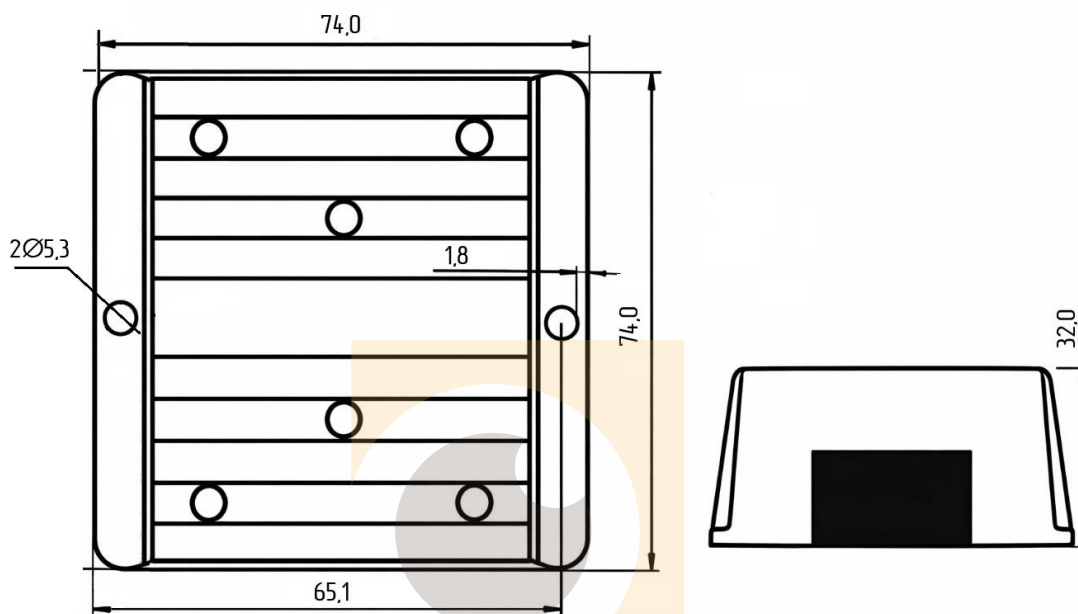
Габаритные размеры бортового преобразователя напряжения CARVIS PS-1210
